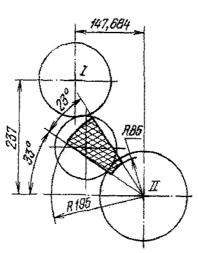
Чертеж для проверки возможности сцепления сменных шестерен на станке 16К25
